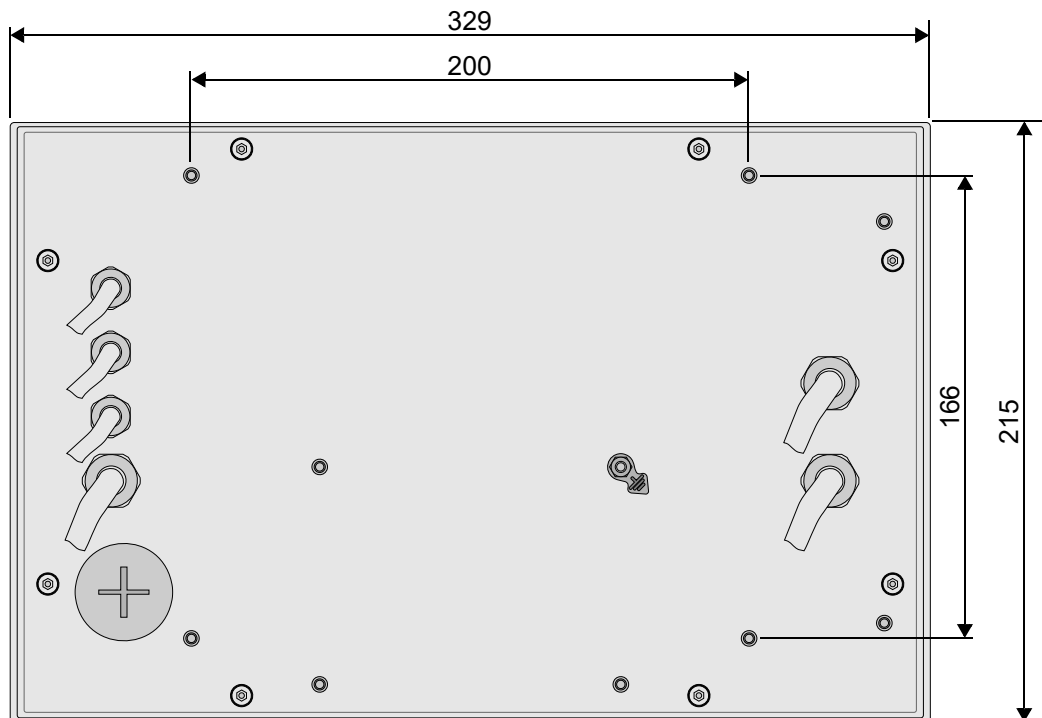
Rückseite des Auswertegerätes mit Positionsangaben für Gewindebolzen
